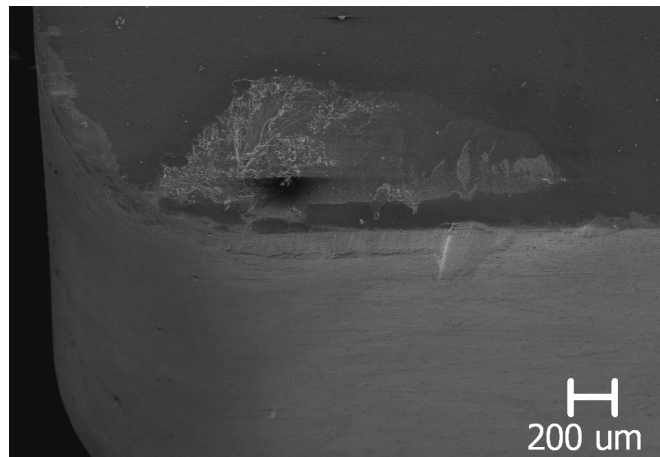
Desgaste apresentado pela ferramenta revestida com TiAlN durante usinagem utilizando MQF 20 ml/h das barras de aço.
